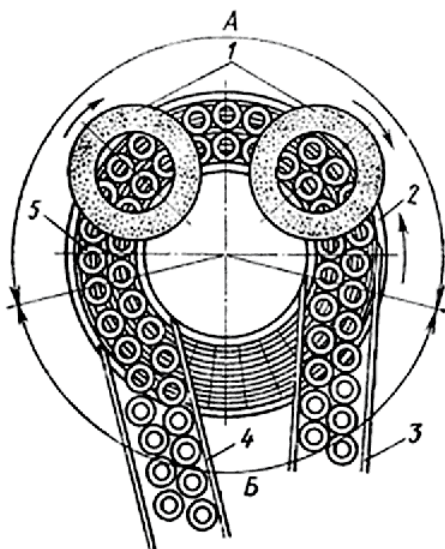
Обработка мелких деталей методом однопроходного шлифования
